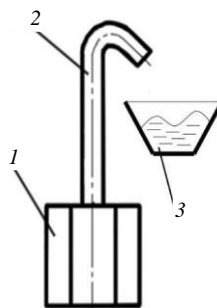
Контрольное приспособление: 1 – гайка; 2 – трубка высокого давления; 3 – емкость
